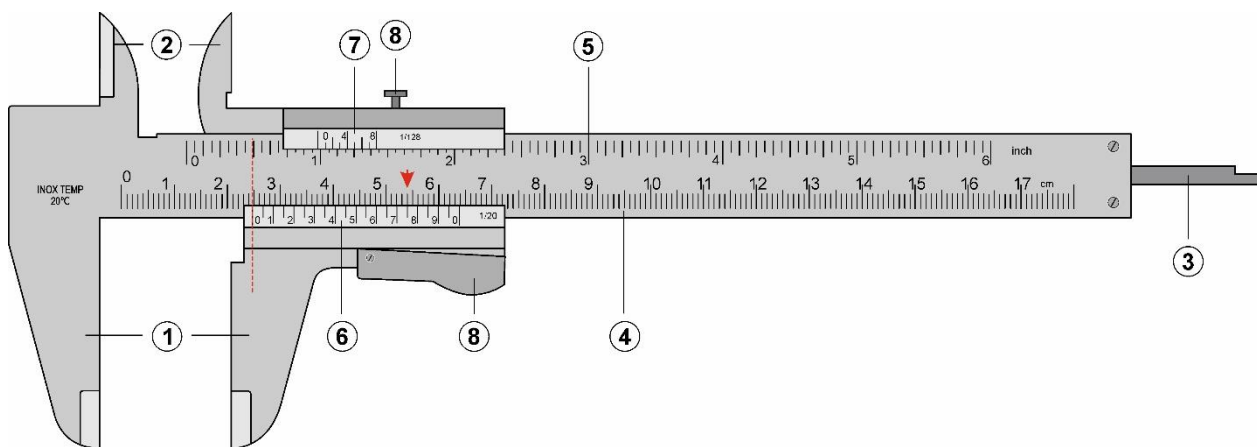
1 – губки для наружных измерений; 2 – губки для внутренних измерений; 3 – линейка глубиномера; 4 – шкала штанги в см; 5 – шкала штанги в дюймах; 6 – шкала нониуса в см, 7 – шкала нониуса в дюймах, 8 – винт для зажима рамки
